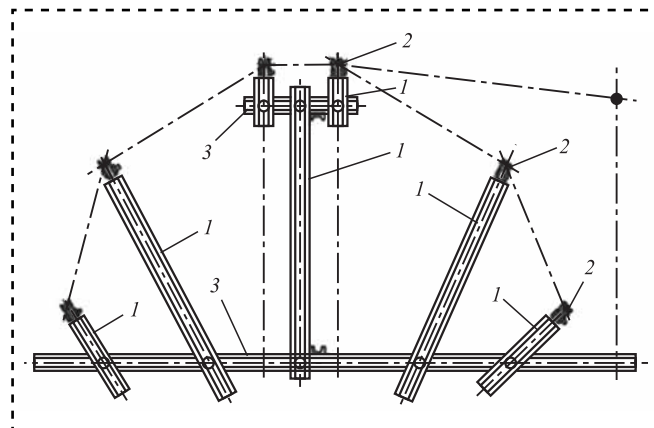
Плоский листовый модуль для формообразования корпуса малого катера:
